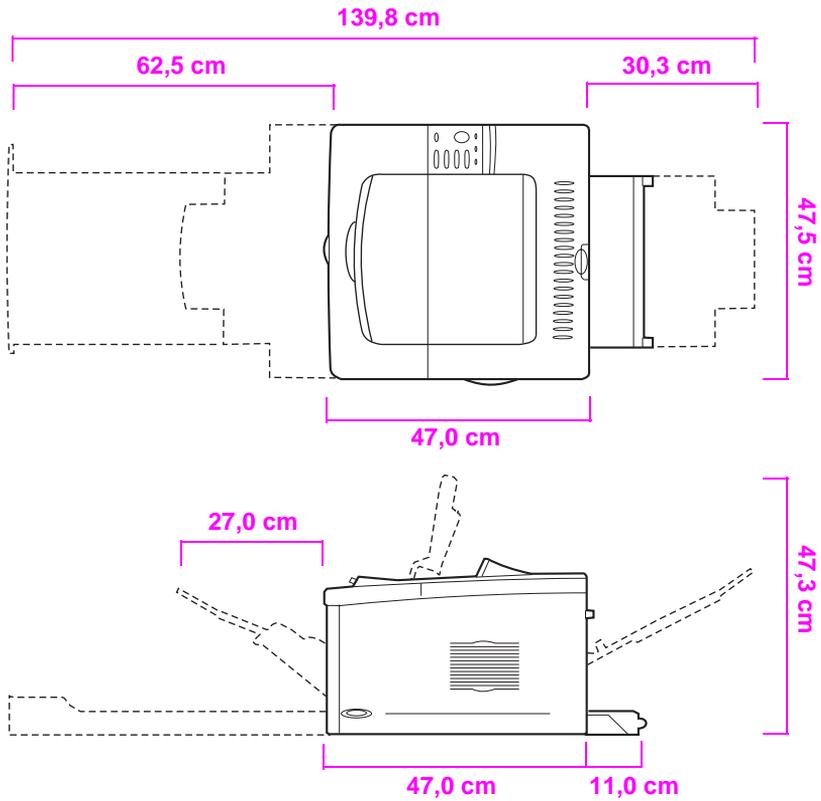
Dimensions de l'imprimante HP LaserJet 5000 (vues supérieure et latérale)
